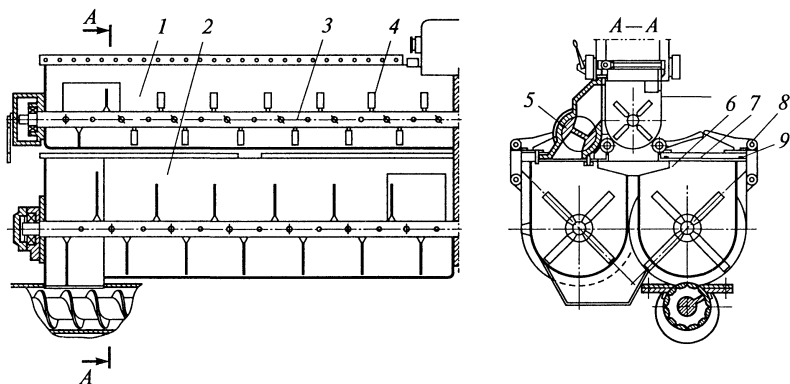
Трехкамерный тестосмеситель макаронного пресса с круглой матрицей
